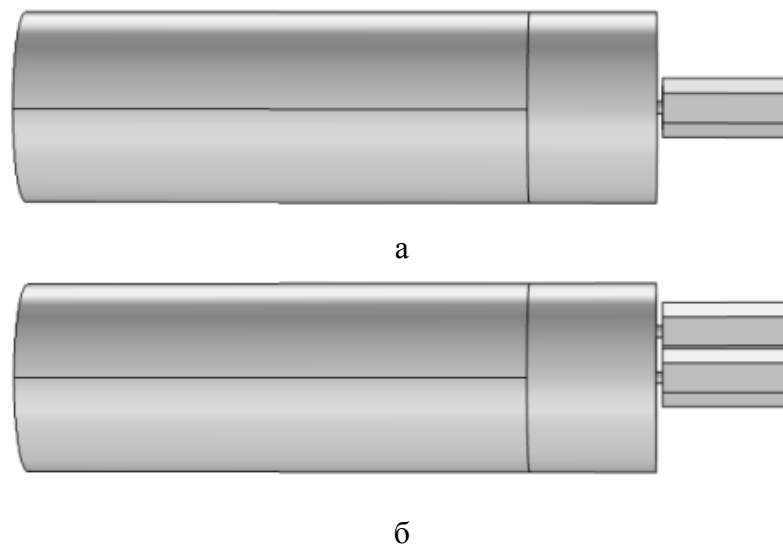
Геометрические модели: а - с единичным резонатором; б - с двумя резонаторами
